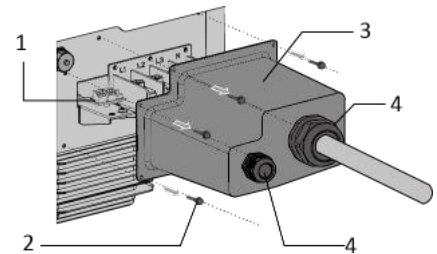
Entfernen Sie die AC/COM-Kunststoffabdeckung
